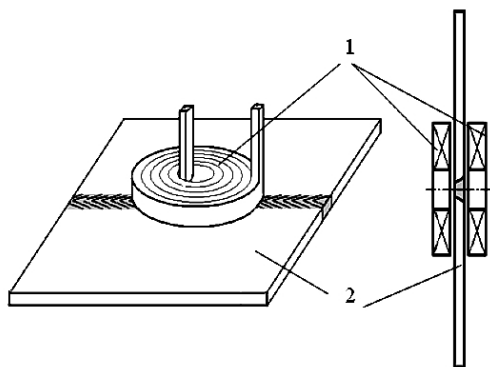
Схема обработки ИЭМП: 1 – индукторы; 2 – пластина со сварным швом.
